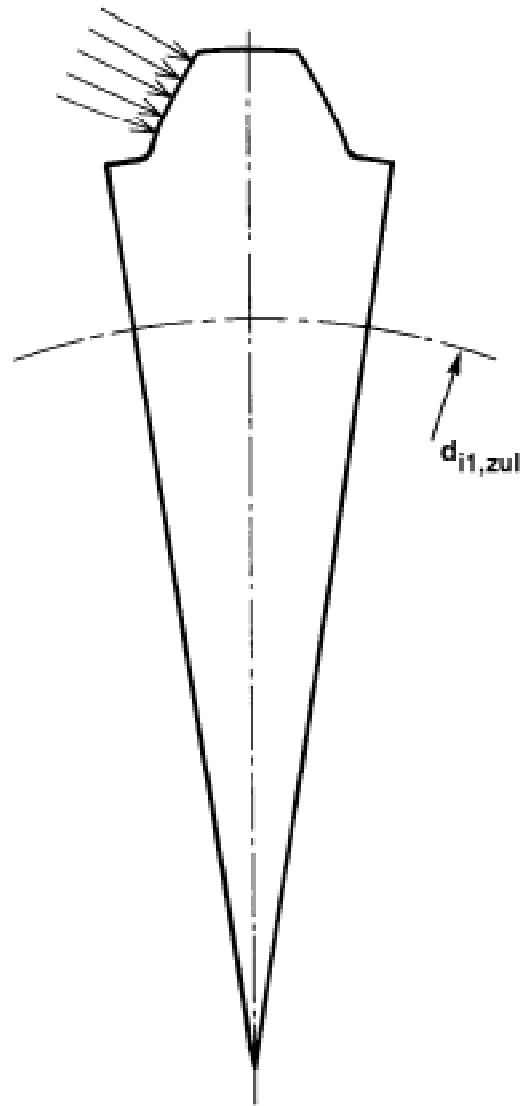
Wellensektor einer Passverzahnung mit zulässigem Innendurchmesser
